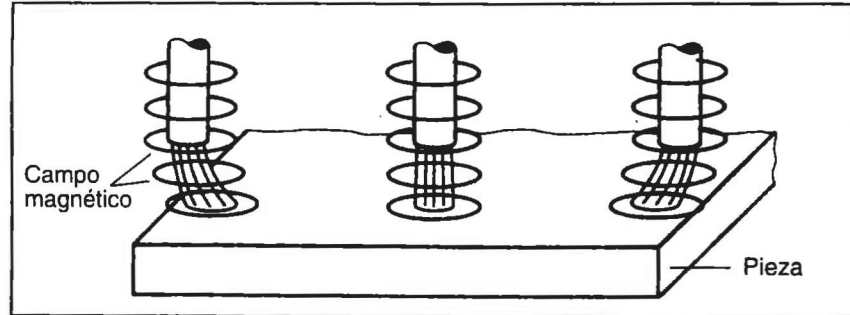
SOPLO MAGNÉTICO AL SOLDAR CERCA DE LOS EXTREMOS DE UNA PIEZA FERROMAGNÉTICA
